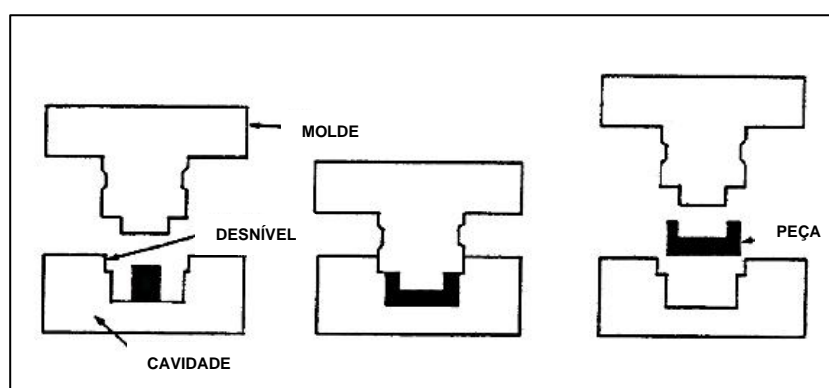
Ilustração do fluxo do material no interior do molde durante a moldagem por compressão.
